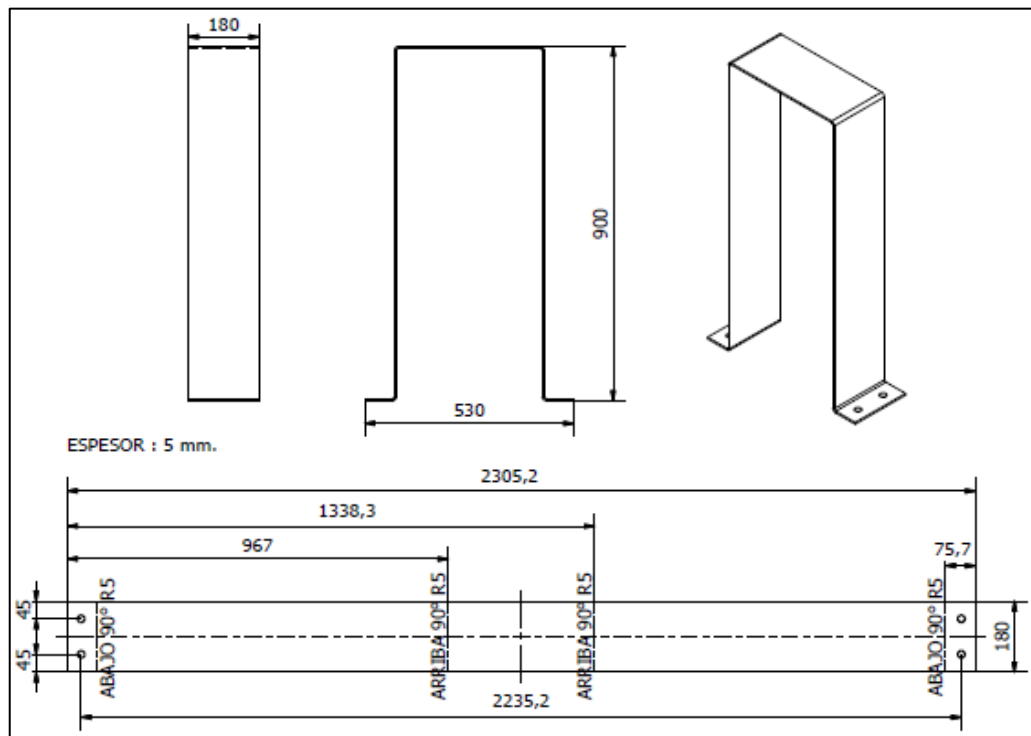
Soporte de Cilindro Neumático DSGB
